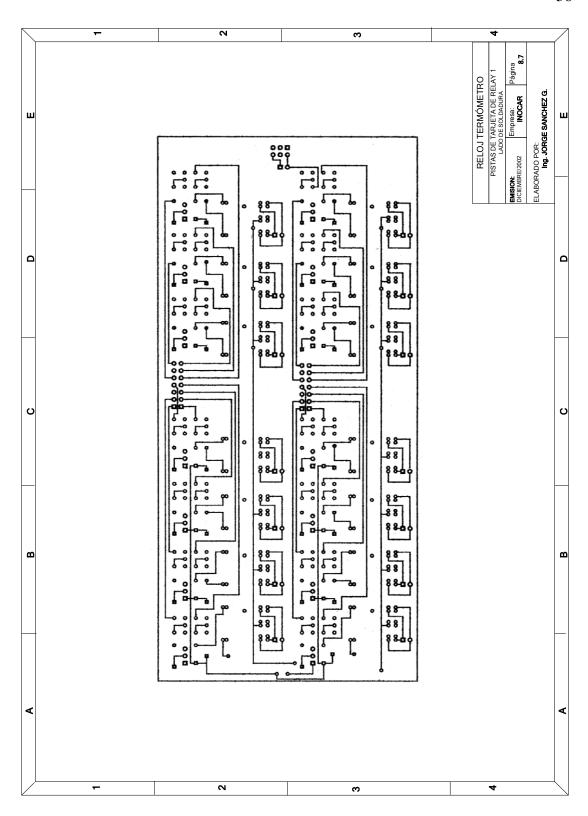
Tarjeta de relay 1 (Pistas lado de soldadura)
